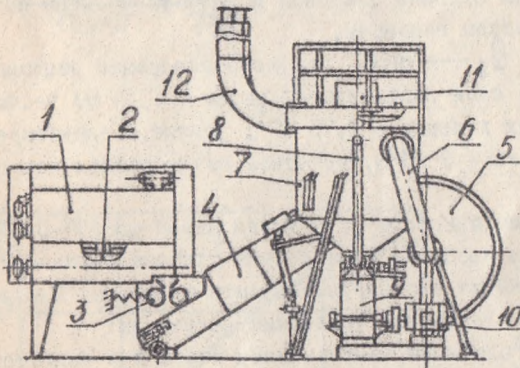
Схема агрегата для сушки кормов АБМ-0,65 с плоскильным устройством:
